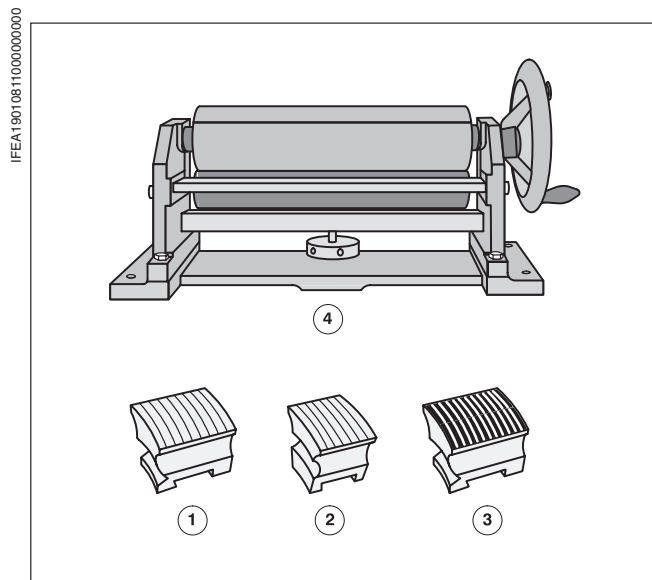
Держатель клише, приспособление для гибки и отбортовки
